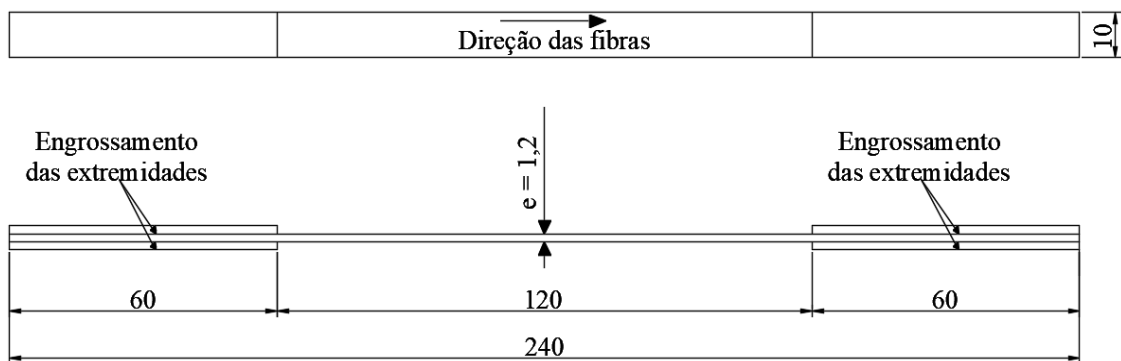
Detalhamento dos corpos de prova do laminado de CFRP (dimensões mm).
